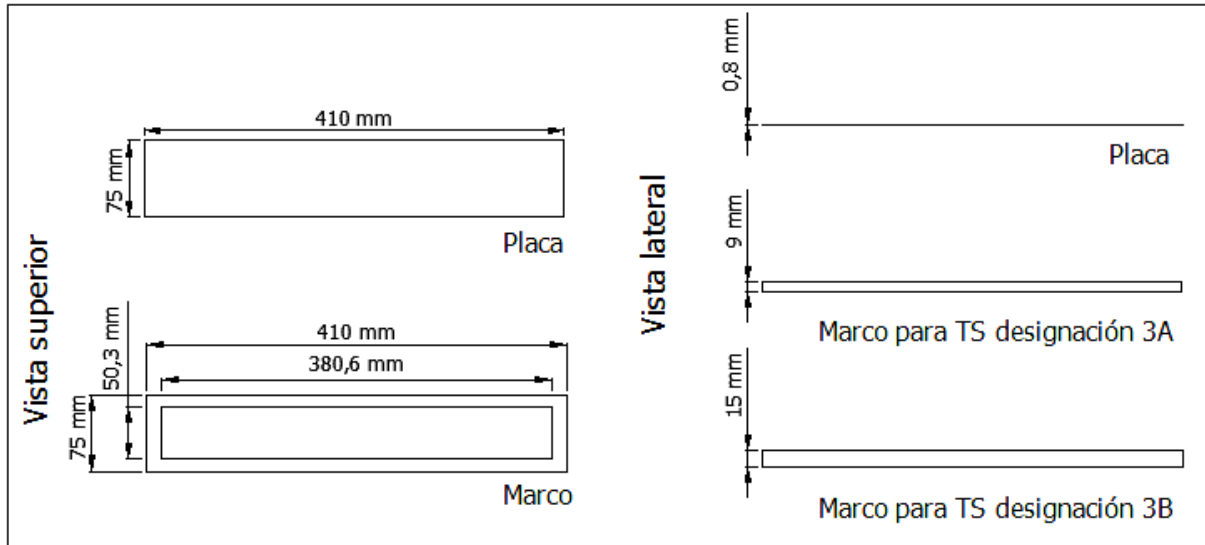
Dimensiones de los moldes para el ensayo de exceso de asfalto
